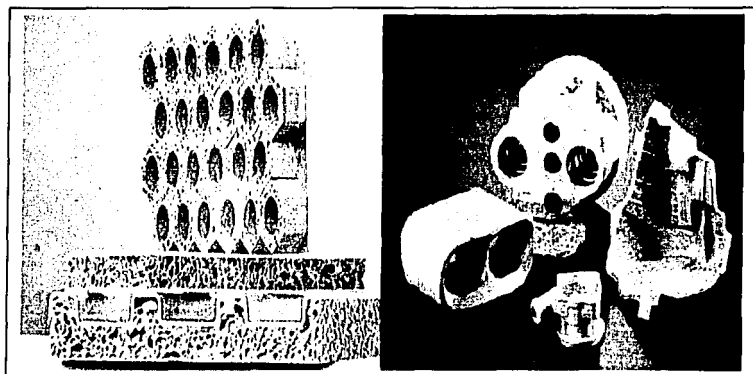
Paneles y estructuras de espumas de aluminio.
